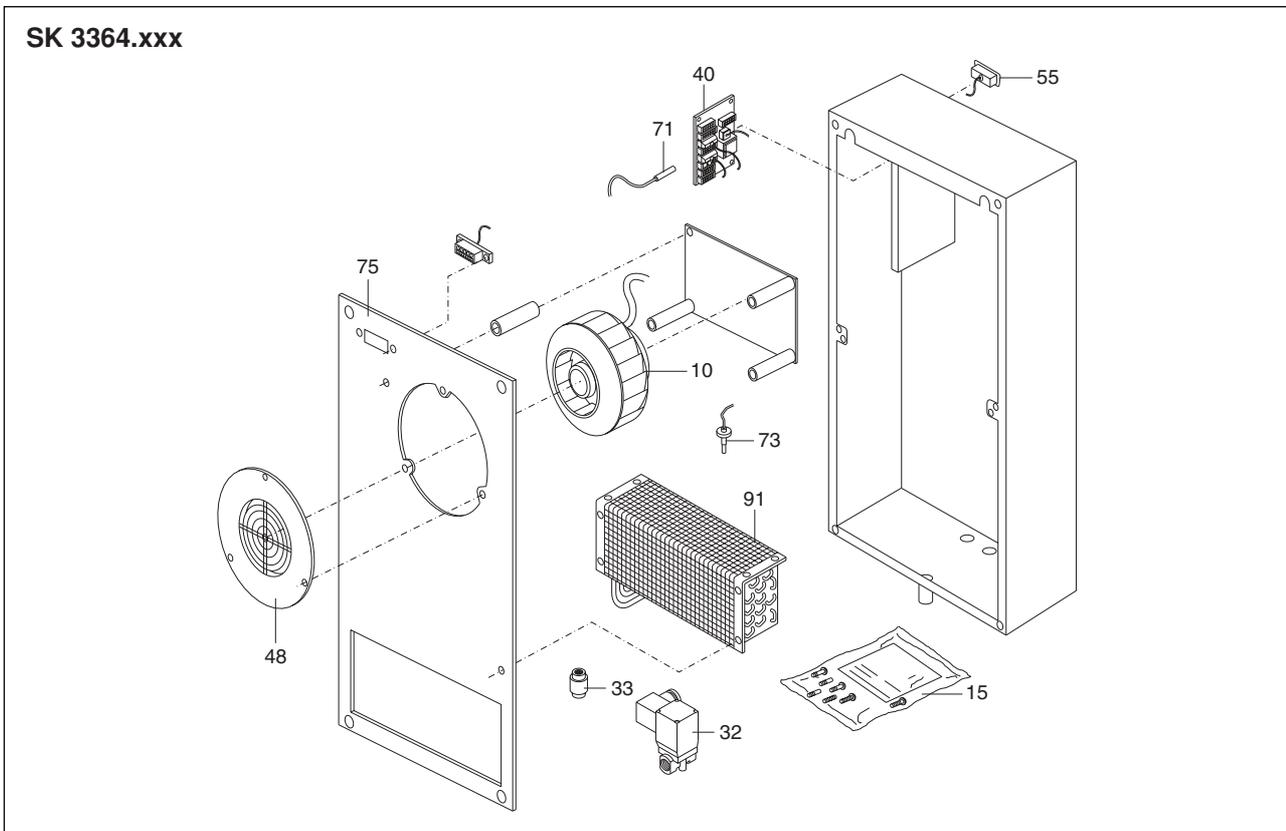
Pièces de rechange pour SK 3364.xxx
